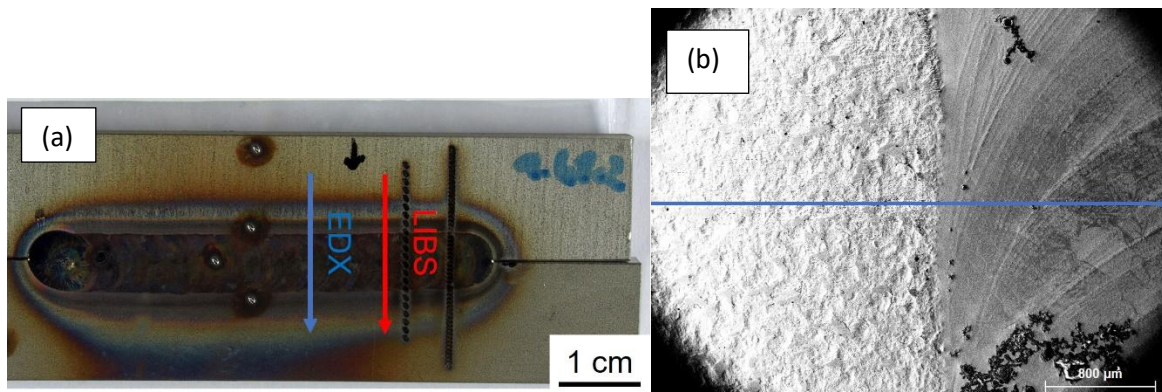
(a) Übersicht einer untersuchten Schweißprobe aus Duplexstahl; Der rote Pfeil kennzeichnet die LIBS-Messungen quer zur Schweißnaht und der blaue Pfeil die EDX-Messungen parallel dazu. (b) REM-Aufnahme einer exemplarischen Stelle, für die Untersuchung. Erkennbar ist der Übergang von WEZ (links) zu SG (rechts). Der blaue Pfeil kennzeichnet die Richtung des EDX-Linescans.
